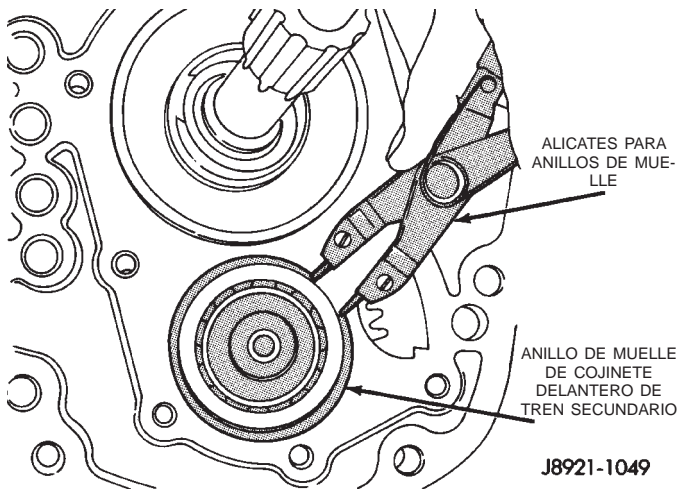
Desmontaje de anillo de muelle del engranaje del tren secundario
